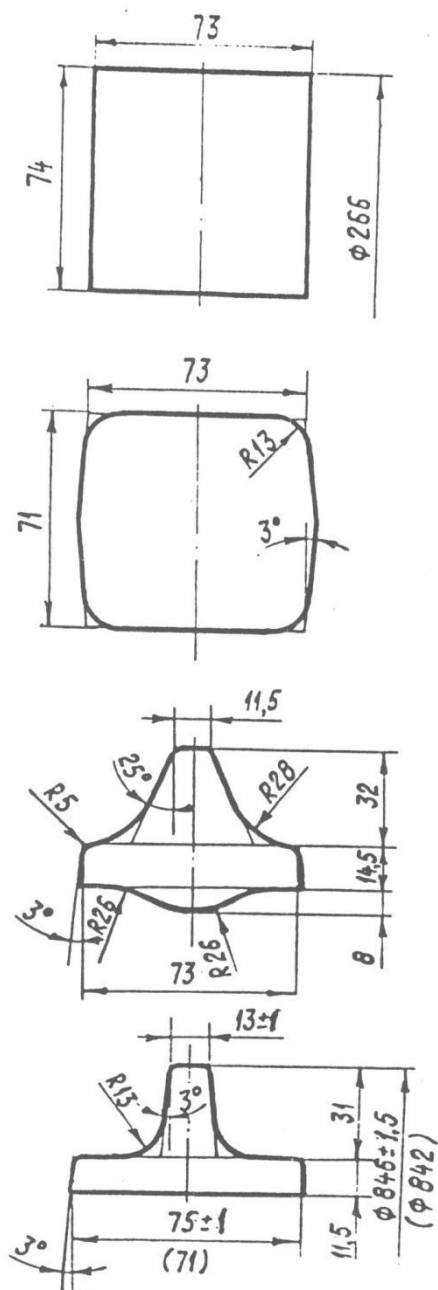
Калибровка заготовки кольца компрессора из сплава ХН45МВТЮБР-
